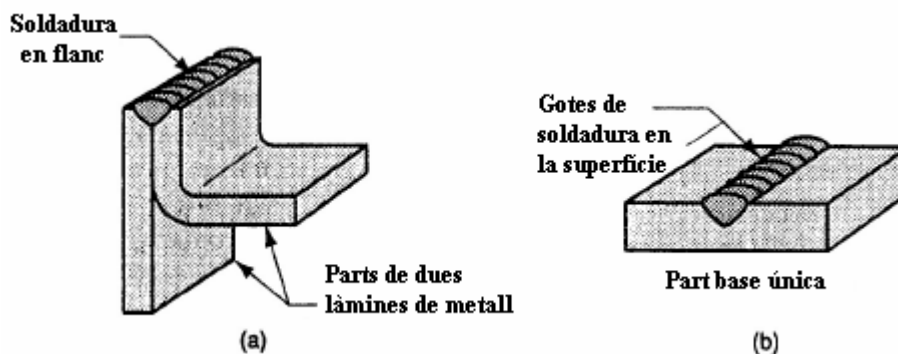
(a) Soldadura en flanc i (b) Soldadura en superfície
